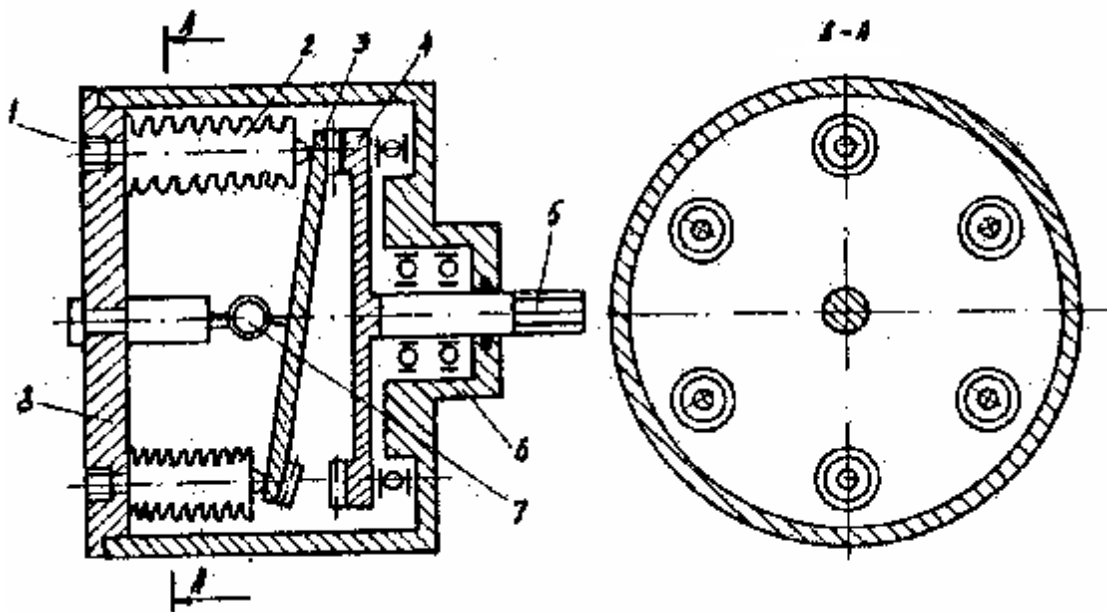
Шеститактный сифонный шаговый гидромотор с конической планетарной передачей
